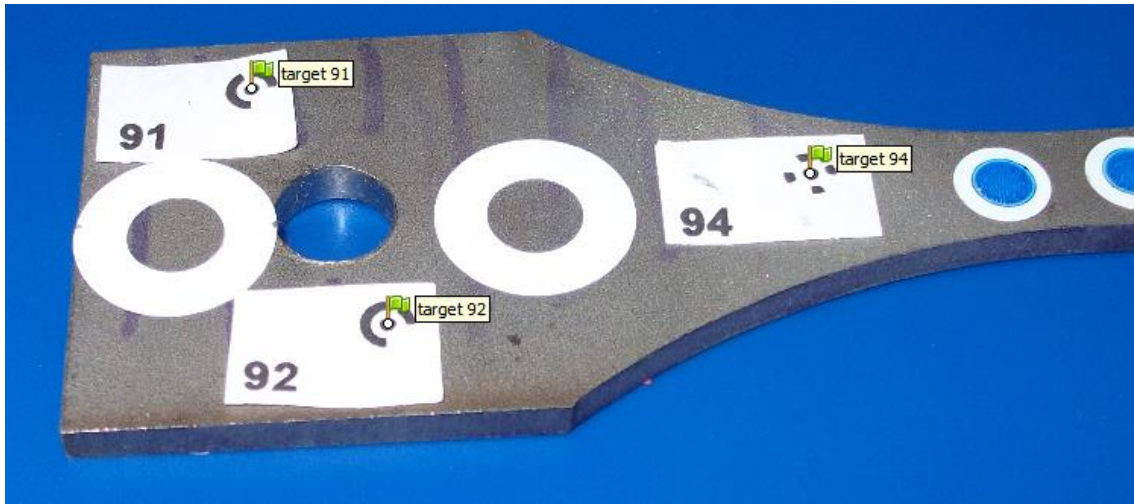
PhotoScan: Identificação de Marcadores numa Fotografia de um Provete de Tracção Metálico, com uma Espessura de 2.46 mm
